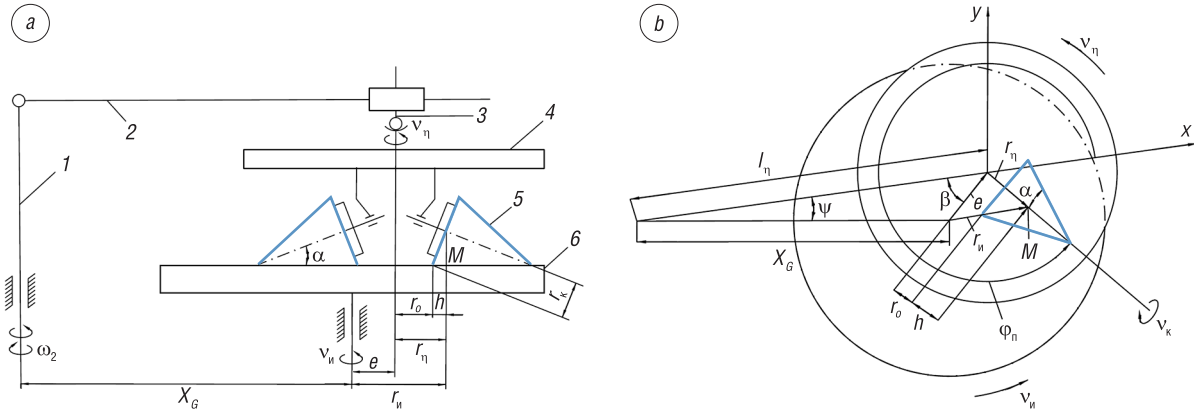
Схема обработки деталей с коническими поверхностями (а) и векторная схема для ее расчета (b)
